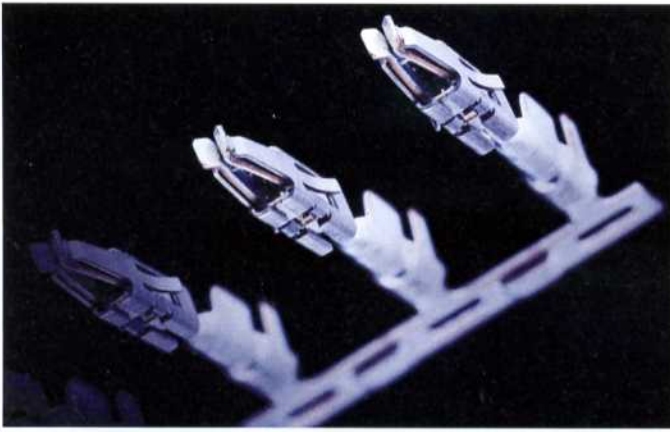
„Ultradlangstreckenläufer“: Mit den Werkzeugen von Schroeder + Bauer werden oft bis zu 2 Milliarden Teile gefertigt.
